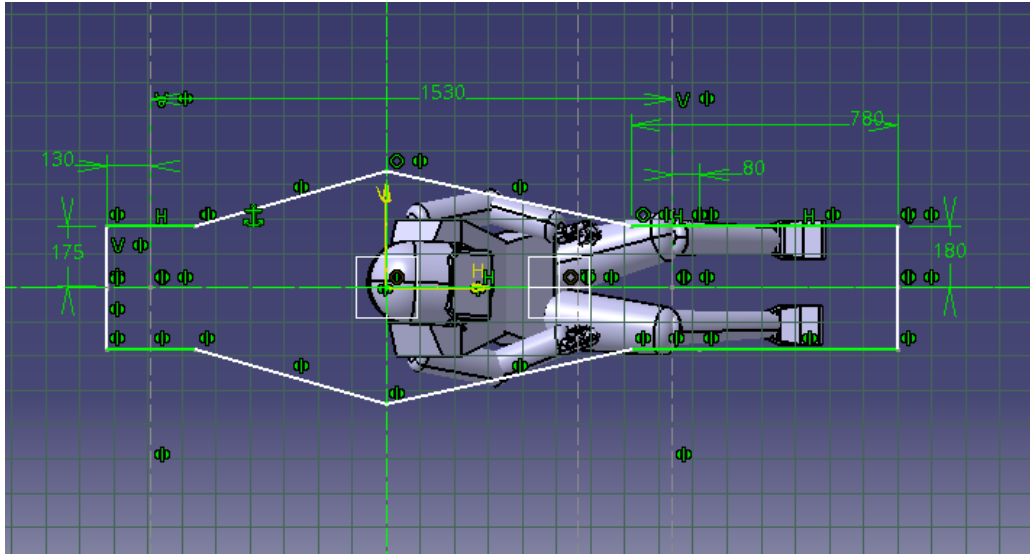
Vista en planta del xassís amb el pilot situat en la posició central. Font pròpia.
